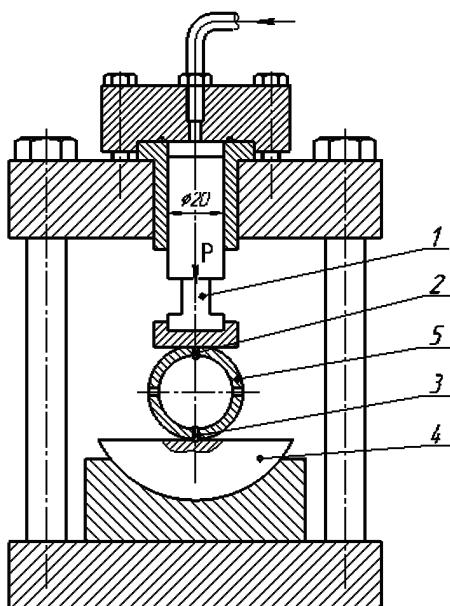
Приспособление для испытаний втулки ПГШ:
